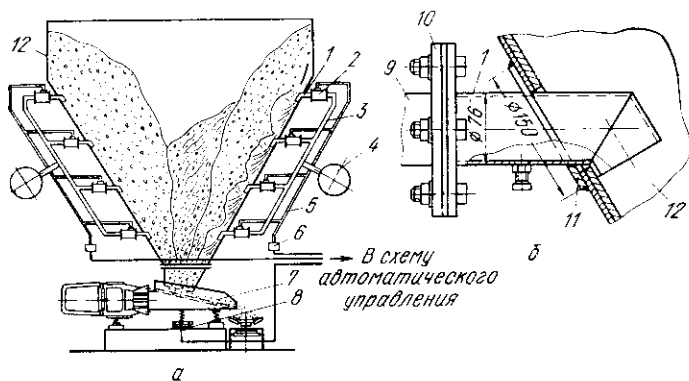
Система автоматического пневмообрушения «микровзрывом»; а — общая схема; б — установка сопла;
